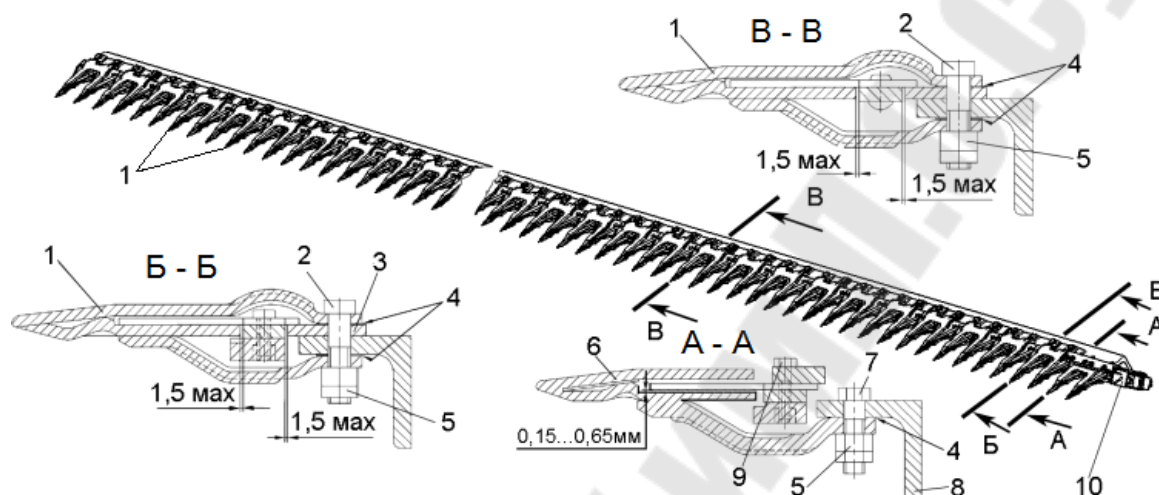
Аппарат режущий: 1 – палец сдвоенный; 2, 7, 9 – болты; 3 – пластина трения; 4 – прокладки регулировочные; 5 – гайка; 6 – палец направляющий сдвоенный; 8 – брус пальцевый; 10 – нож с головкой
